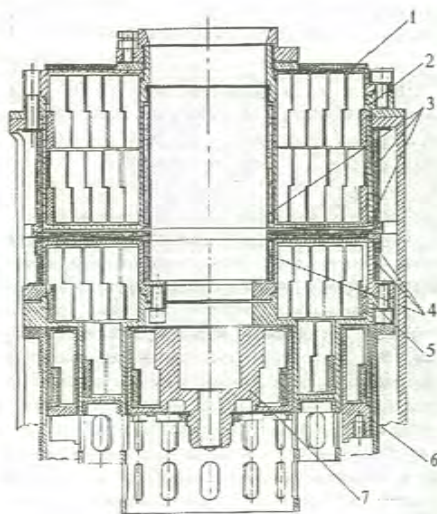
Схема АЗ реактора БР-1 в осевом разрезе: 1 – фильтр из В₄С; 2 – верхний блок; 3, 4 – фильтры из ¹⁰В; 5 – нижний блок; 6 – регулирующий блок; 7 – импульсный блок.
